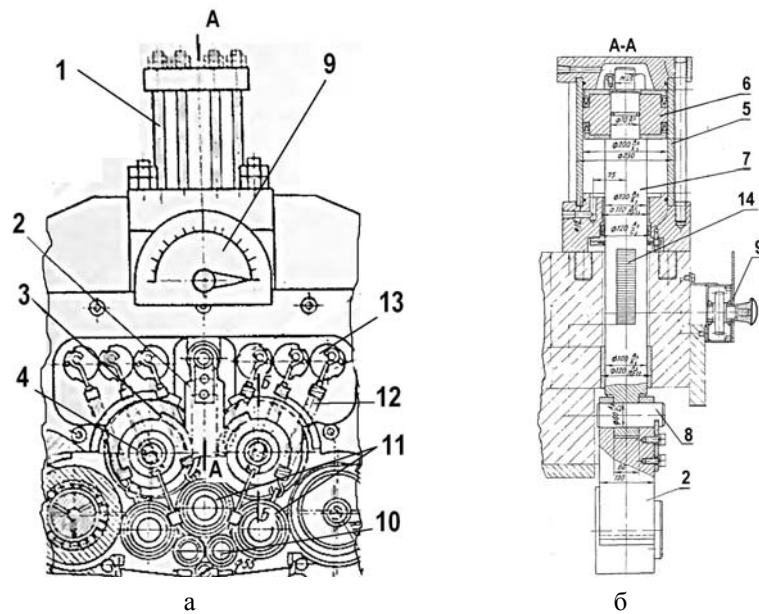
верхній натискний механізм (а) та конструкція натискного гідроциліндру (б)
